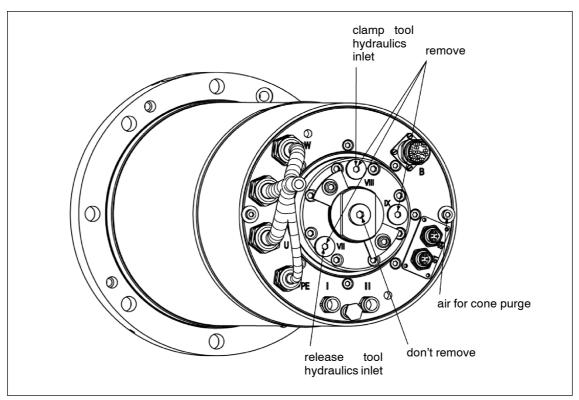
ECS-M idraulico 2SP120 -1H 3 - senza distributore rotante
